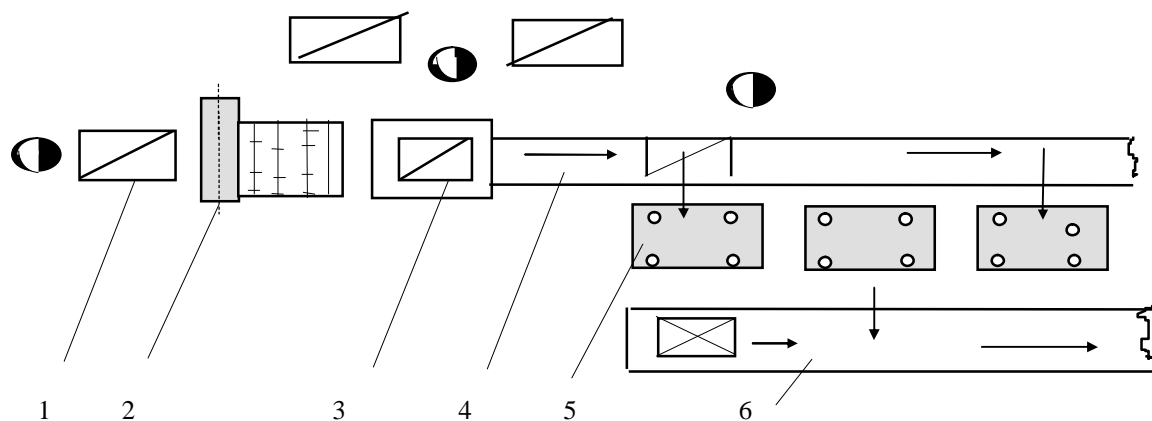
Схема участка изготовления гнукотклееных заготовок: 1 - стопа шпона, 2 - клеенаносящий станок, 3 - сборочный конвейер, 4 - конвейер подачи пакетов к прессам, 5 - прессы, 6 - конвейер заготовок.
